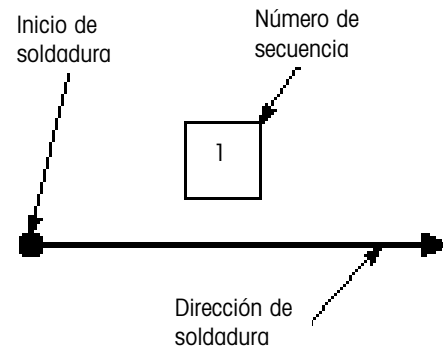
Leyenda de instrucciones de soldadura
